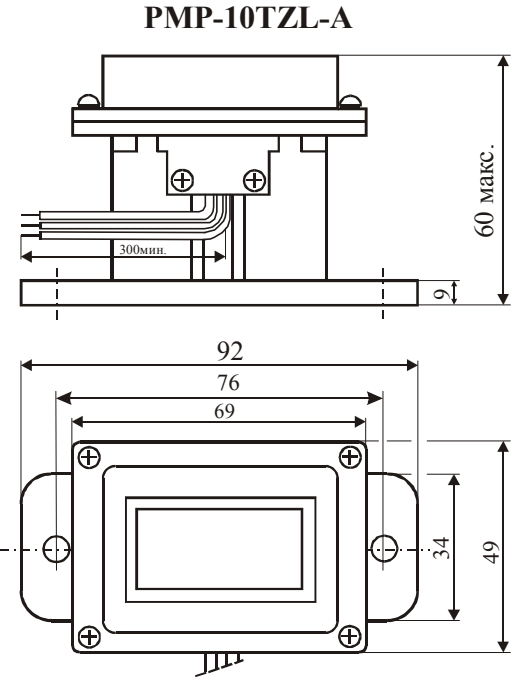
Внешний вид и габаритные размеры датчика угла наклона типа PMP-10TZL-A
